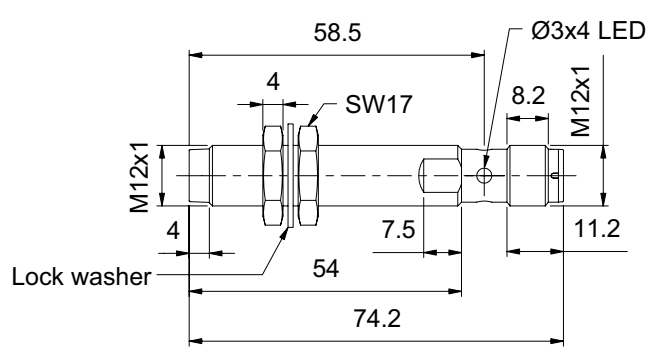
Uskærmet, ikke planmontage, M12-stik
